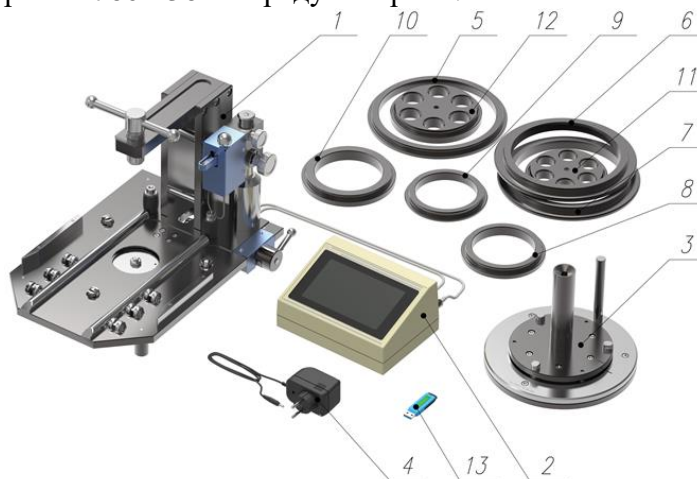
Общий вид прибора для контроля осевого зазора кассетных подшипников модели БВ-7602-36. Прибор состоит из: 1 - станции измерительной, 2 – электронного блока, 3 – калибровочной меры, 4 – сетевого адаптера, 5 – 12 – оправок, 13 – флэш-накопителя.
